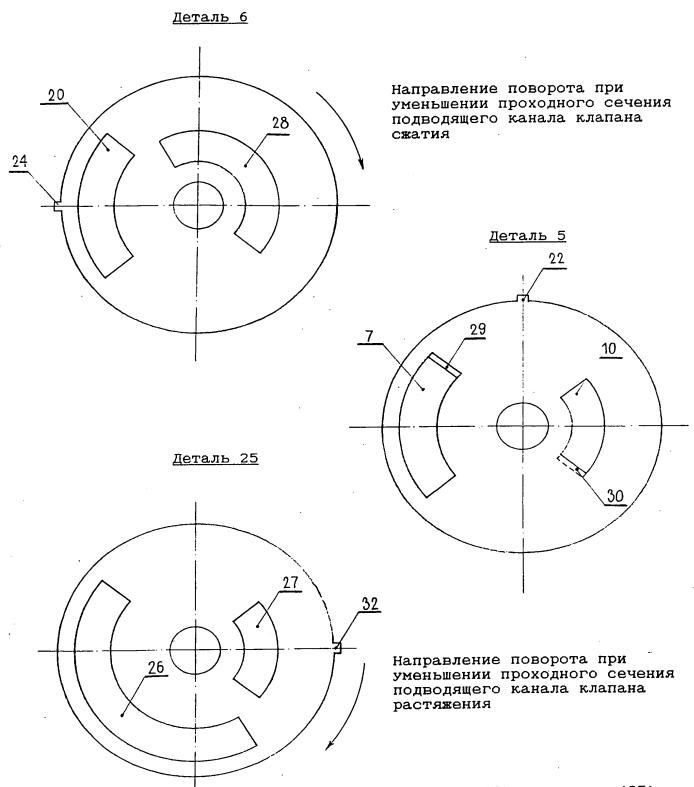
Вид сверху на деталь (5) и деталь (6) устройства, изображенного на фиг.1.
